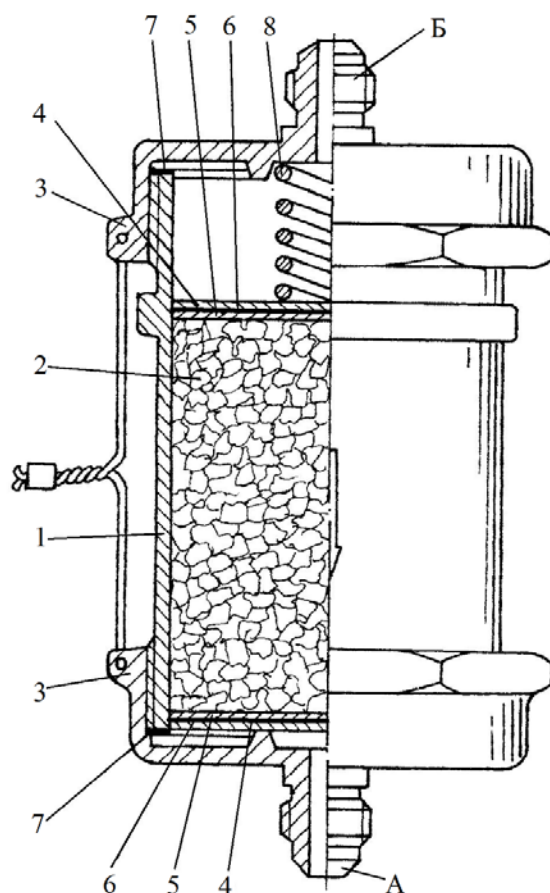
Фильтр – влагопоглотитель, где 1- корпус; 2- силикагель; 3- крышка; 4- шайба; 5- сетка; 6- фильтровальная бумага; 7- кольцо; 8- пружина
